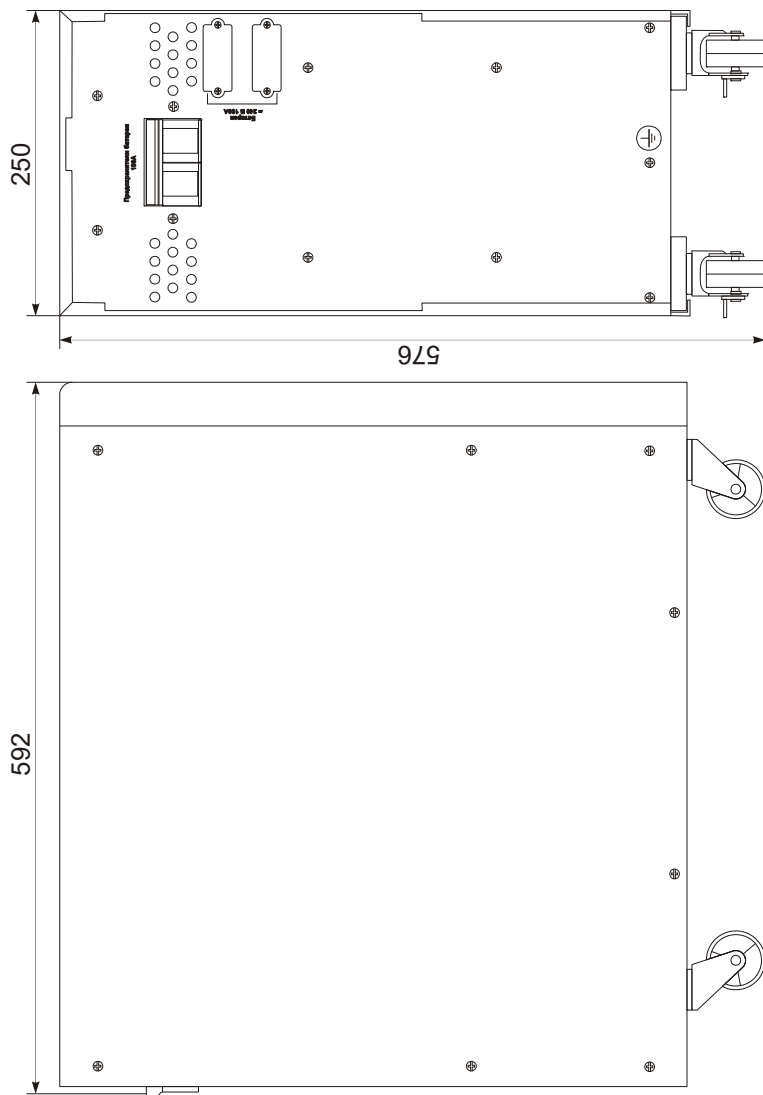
Габаритные и установочные размеры БМ ВР 240-18-100А
